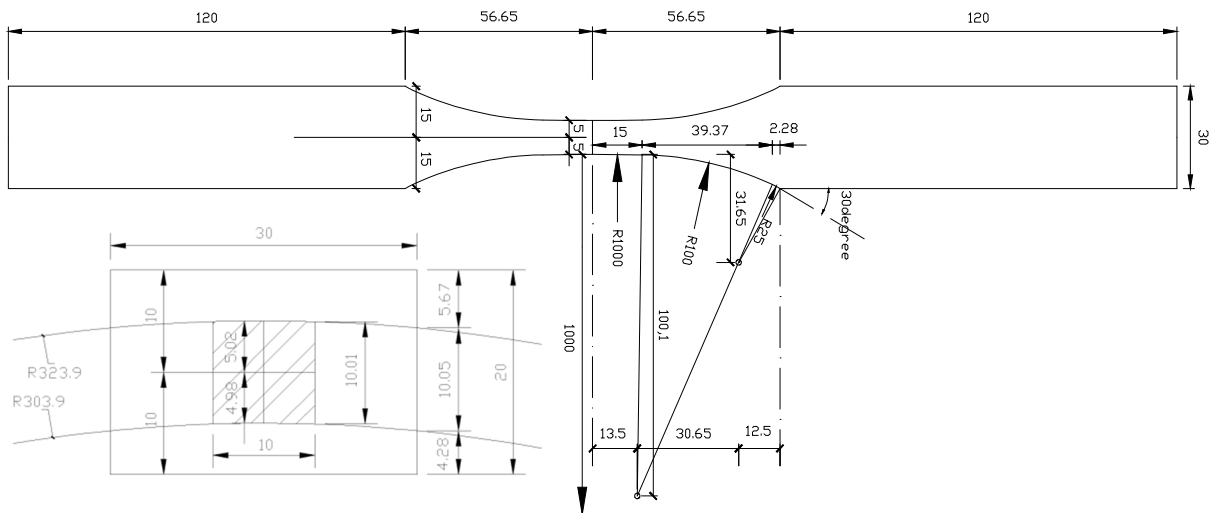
Probenabmessungen - Draufsicht und Frontansicht
